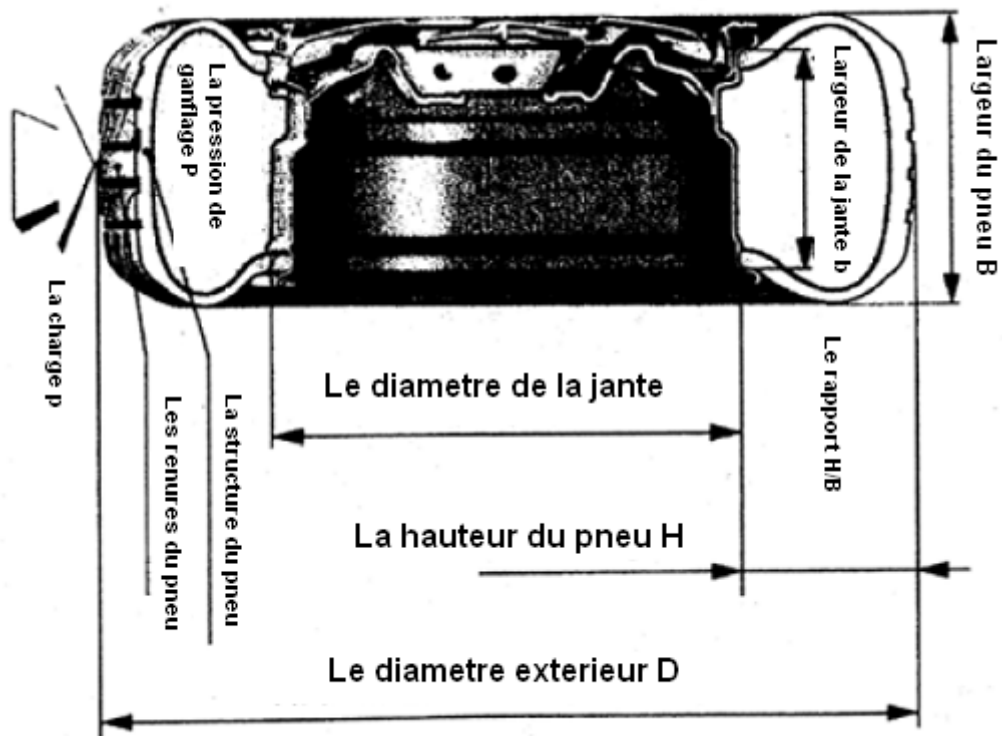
Les dimensions importantes d'un pneumatique [5]
